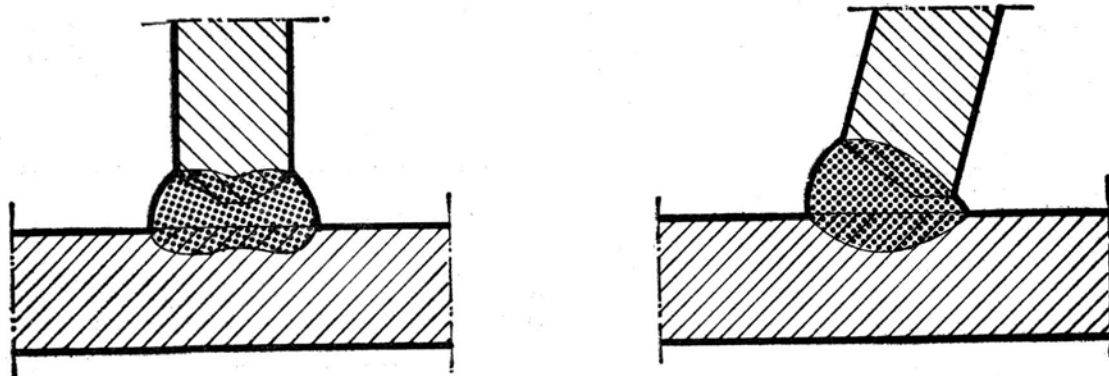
SOLDADURAS A TOPE, EN T
